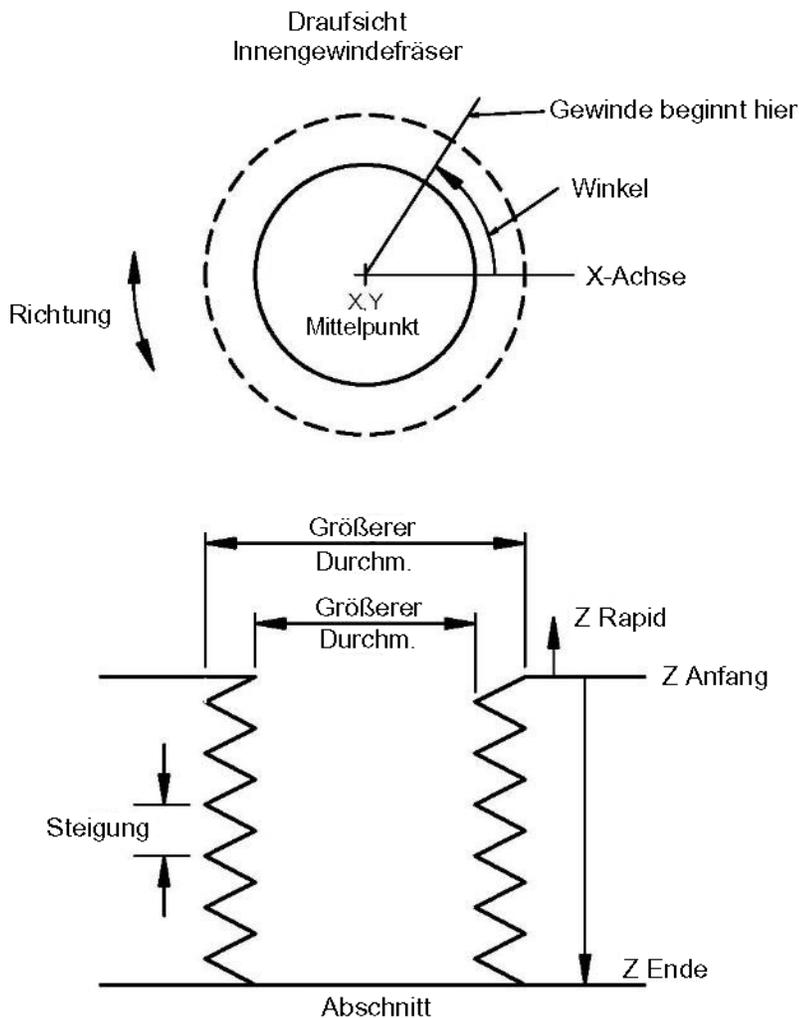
Eingabeaufforderungen für Gewinde
